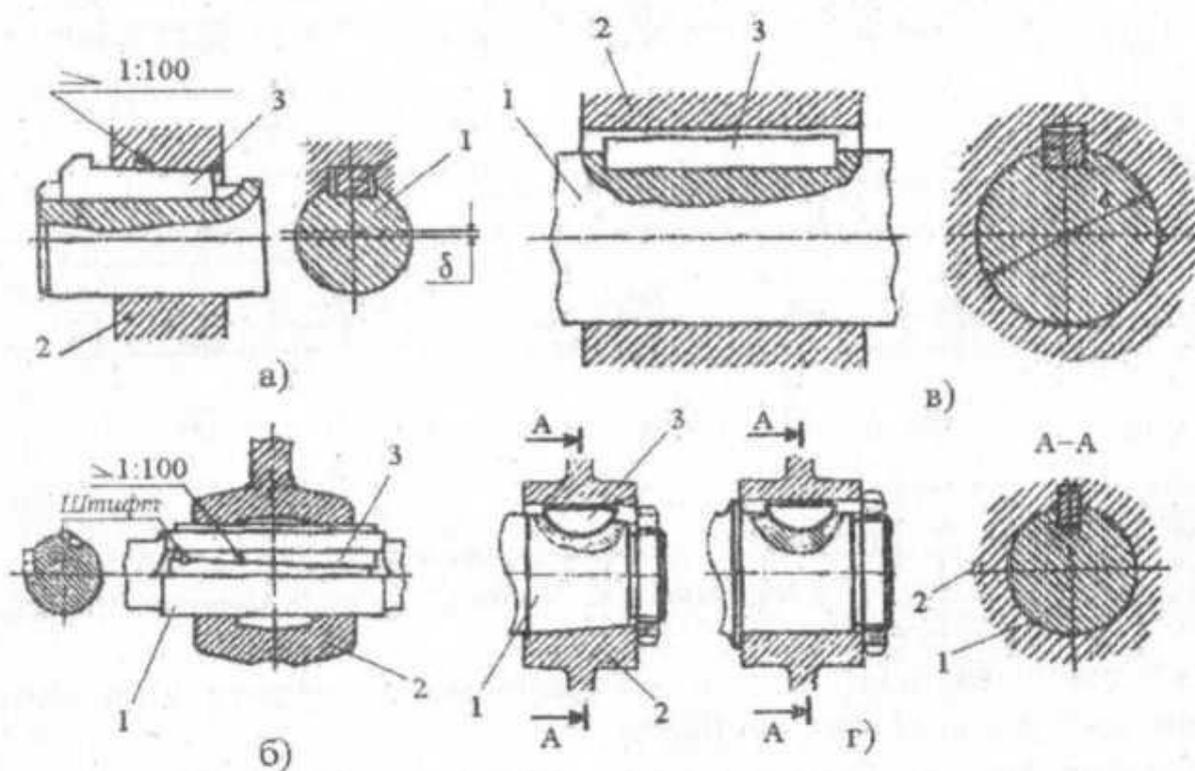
Шпоночные соединения деталей: а – клиновой шпонкой; б – тангенциальными шпонками; в – призматической шпонкой; г – сегментной шпонкой; 1 – вал; 2 – ступица детали; 3 – шпонка
